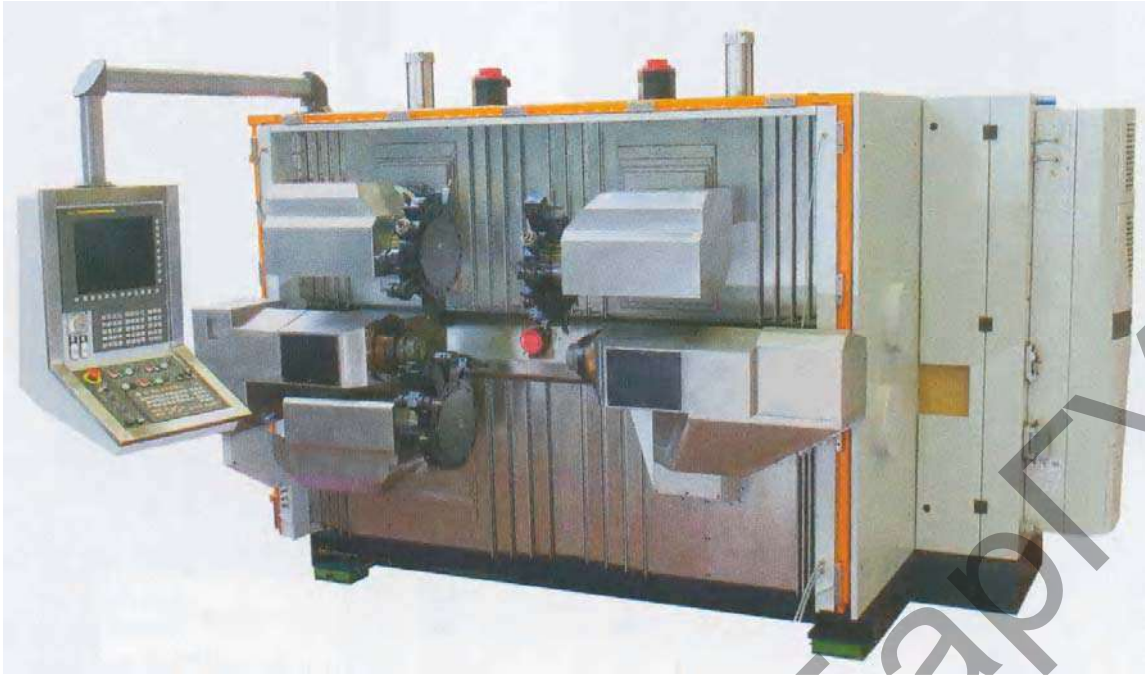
Токарный обрабатывающий центр серии TD42-Triplex (без защитного ограждения) с двумя шпинделями и тремя револьверными головками. Компания SPINNER (Германия)
